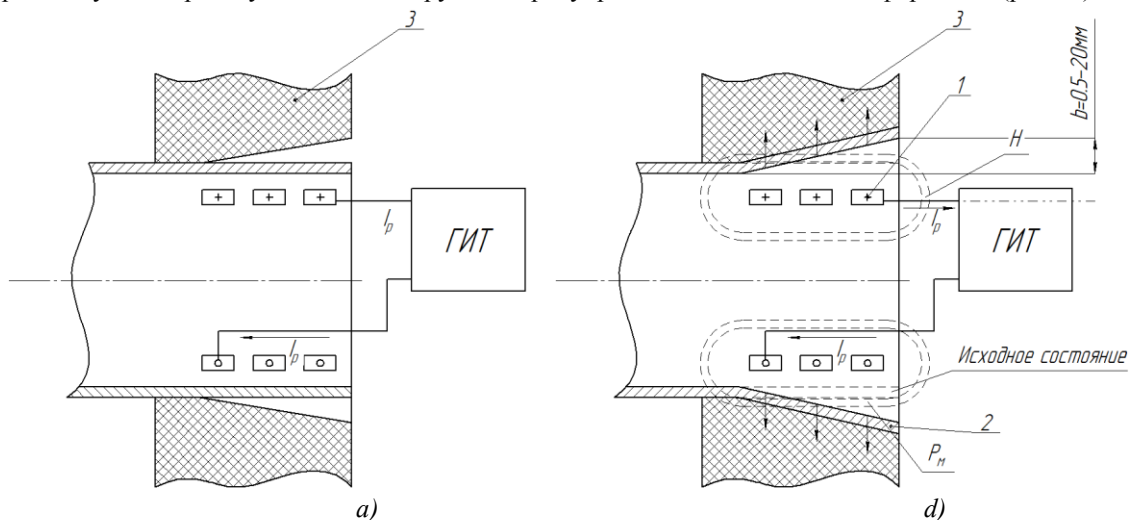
Схема магнитно-импульсной обработки для раздачи под сварку:
